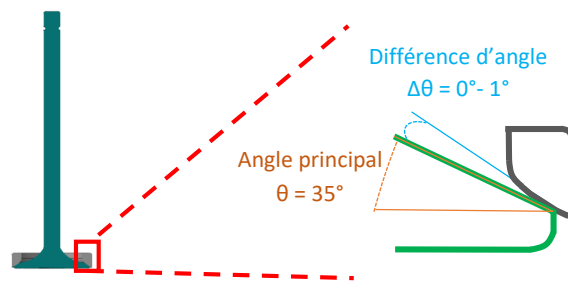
Les deux angles du contact siège-soupape, θ l'angle fixant la géométrie globale du contact, $\Delta\theta$ tolérance de la production pour imposer le contact en bas de la portée
